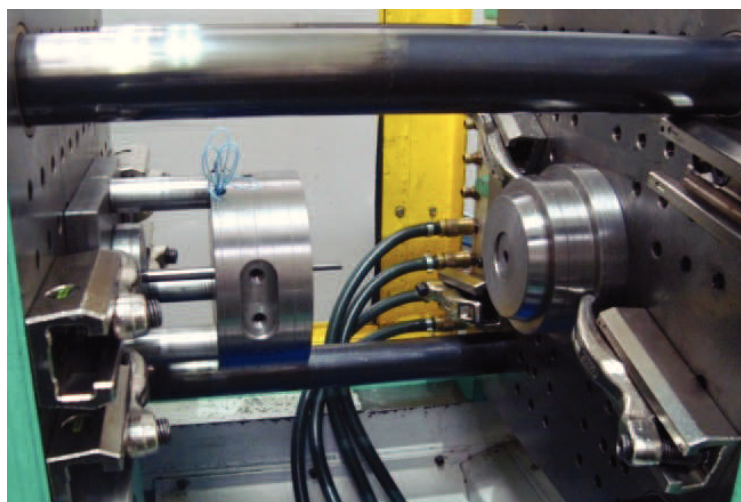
Pormenor de montagem do molde protótipo na máquina de injeção.
